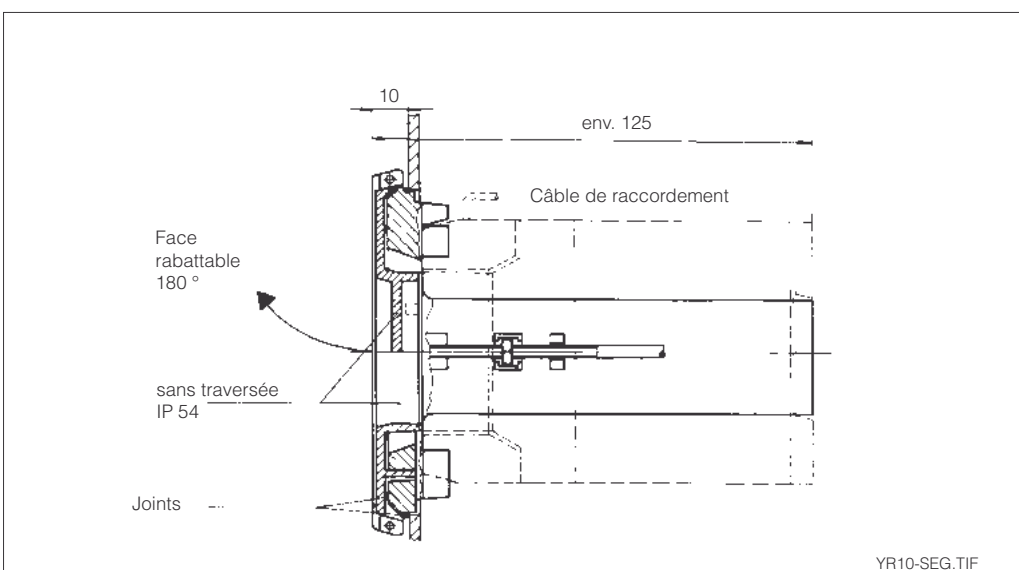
Dimensions cadre de montage SEG pour CYR 20
